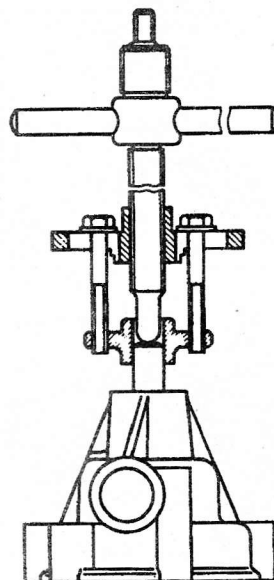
Выпрессовка подшипника с валиком водяного насоса
